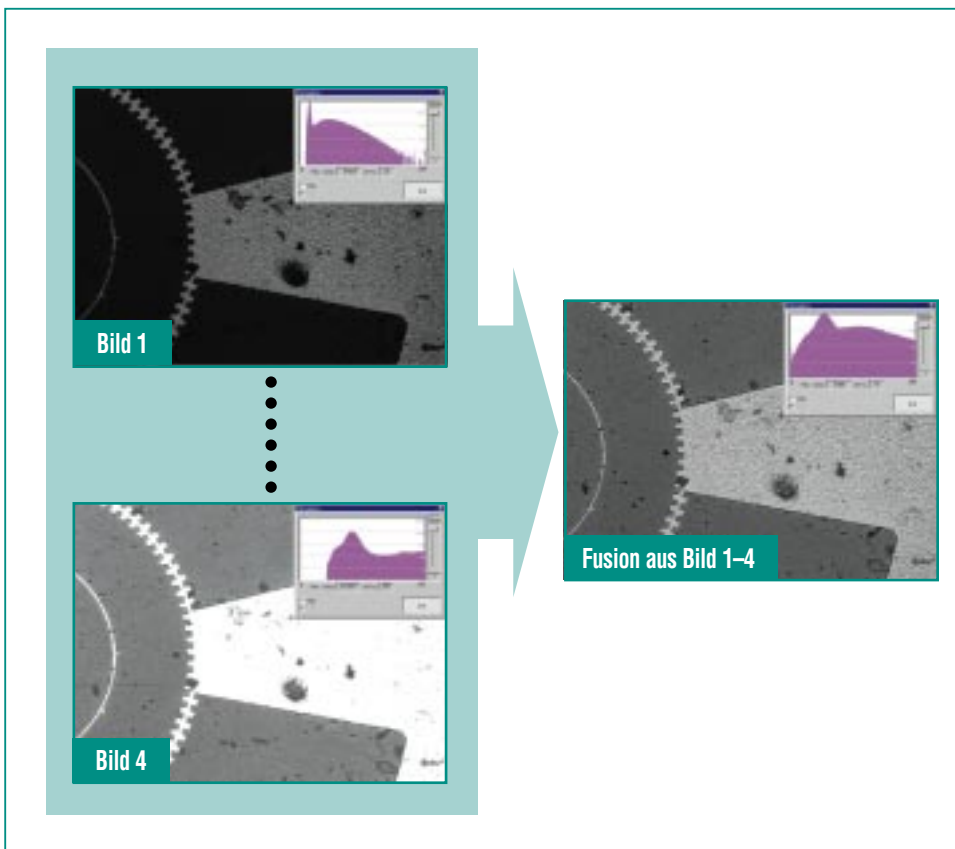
Bildrekonstruktion aus einer Beleuchtungsserie mit insgesamt vier Bildern.
